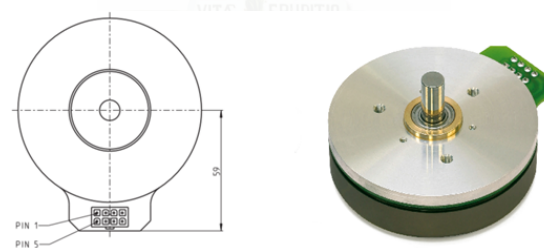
Motor EC 90, esquema a la izquierda, aspecto del motor a la derecha
